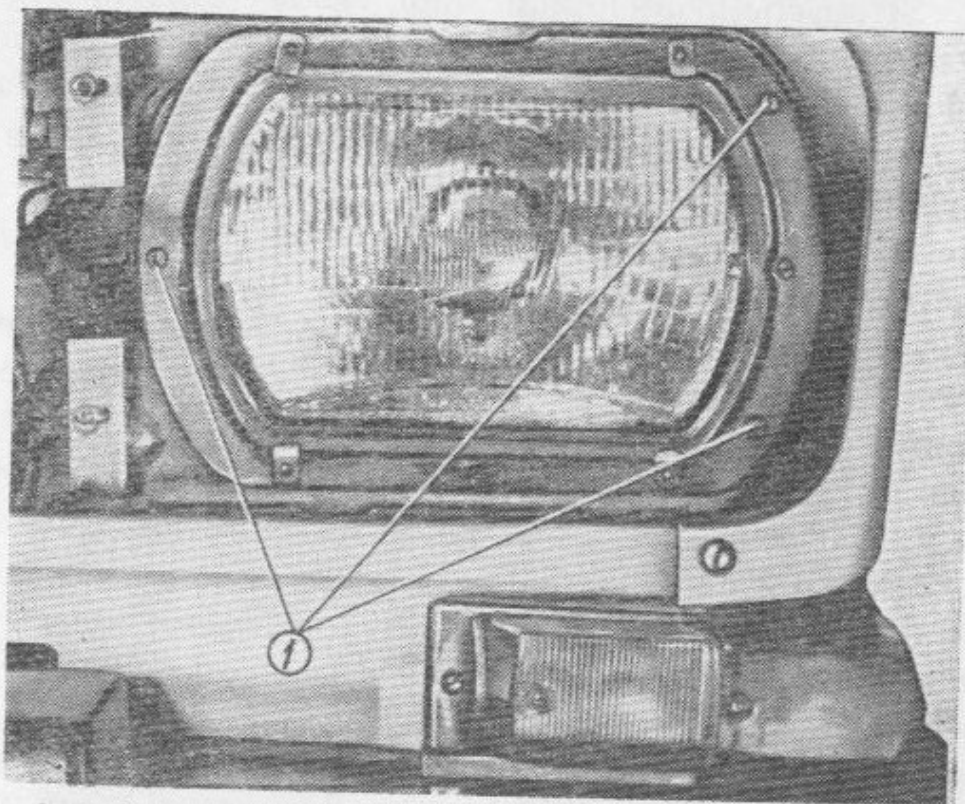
Anordnung der Schrauben für Befestigung des Scheinwerfers an Karosserie:
